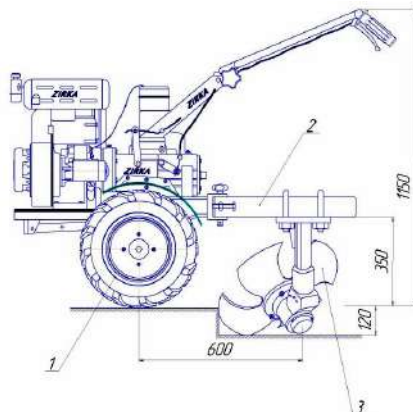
Дослідний зразок ґрунтообробного агрегату: 1 – мотоблок; 2 – начіпний пристрій; 3 – корпус дисковий
